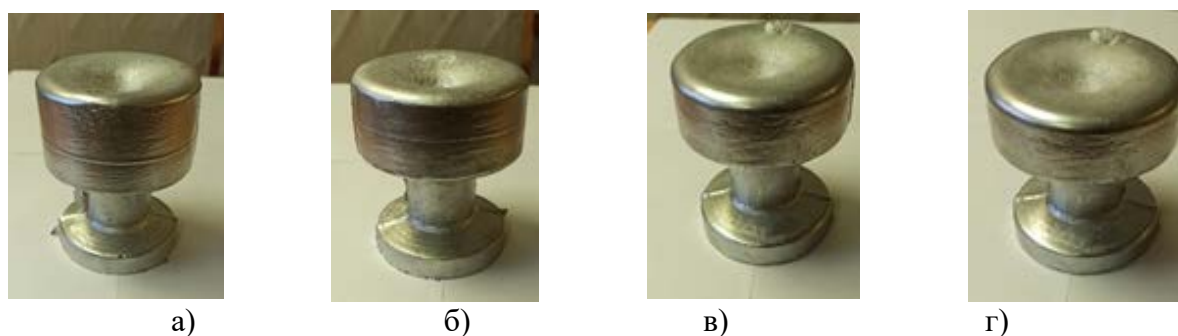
Опытные отливки с различной высотой прибыльной части:
